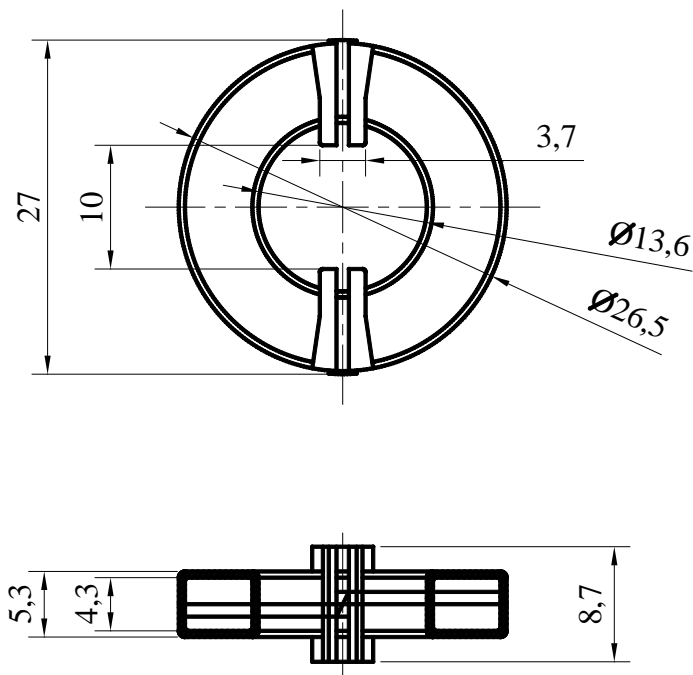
Внешний вид и габаритные размеры магнитопровода MSFN-25B-TH1
